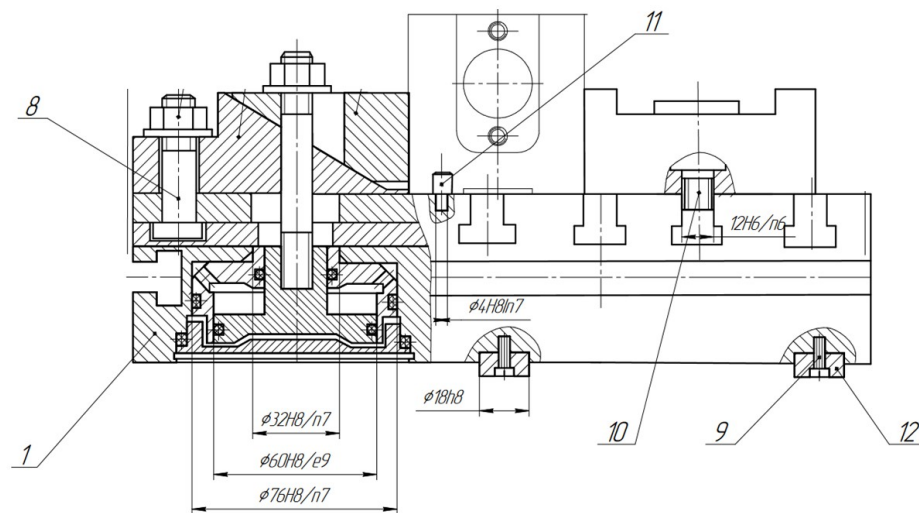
Загальний вигляд верстатного пристрою
